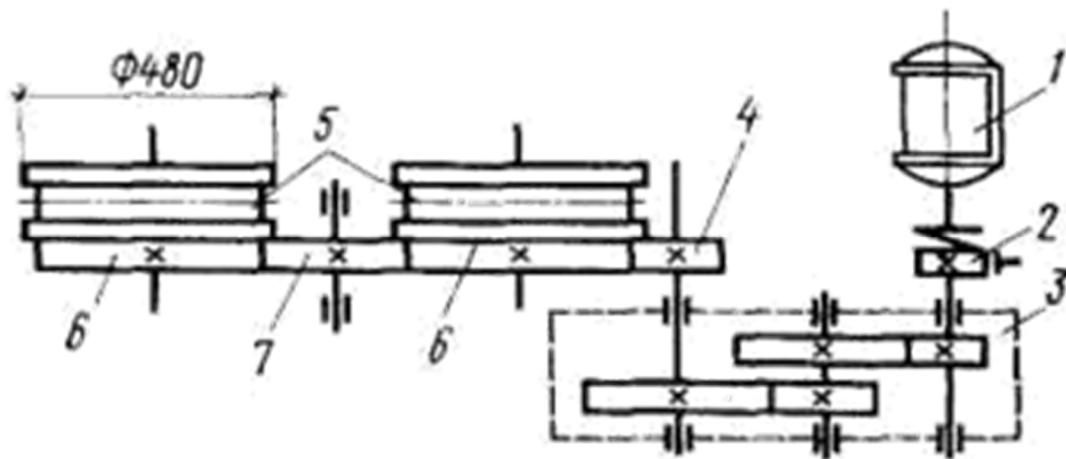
Кінематична схема ходового пристрою з жорсткими металевими колесами:
